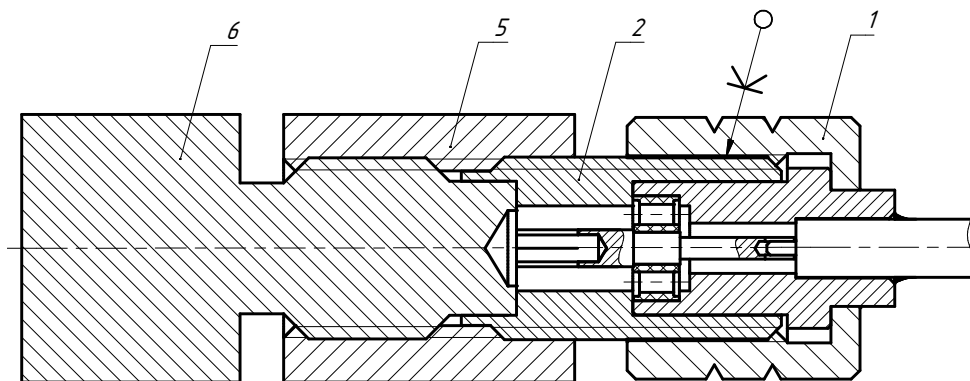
Монтаж соединителя с использованием приспособления ЖНКЮ.296371.030-02
